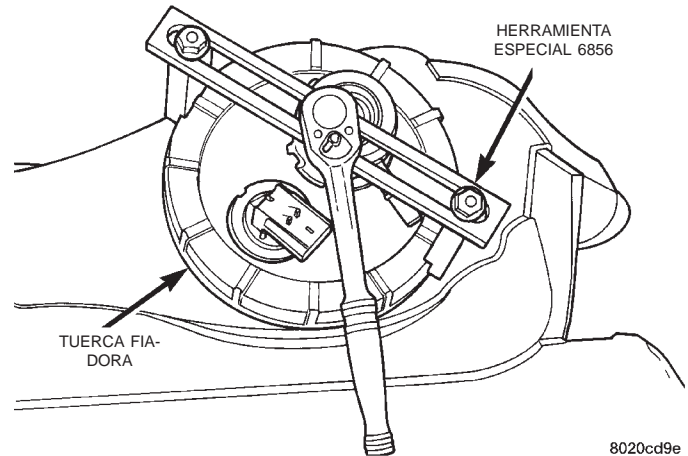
Desmontaje e instalación de tuerca fiadora—Característico
